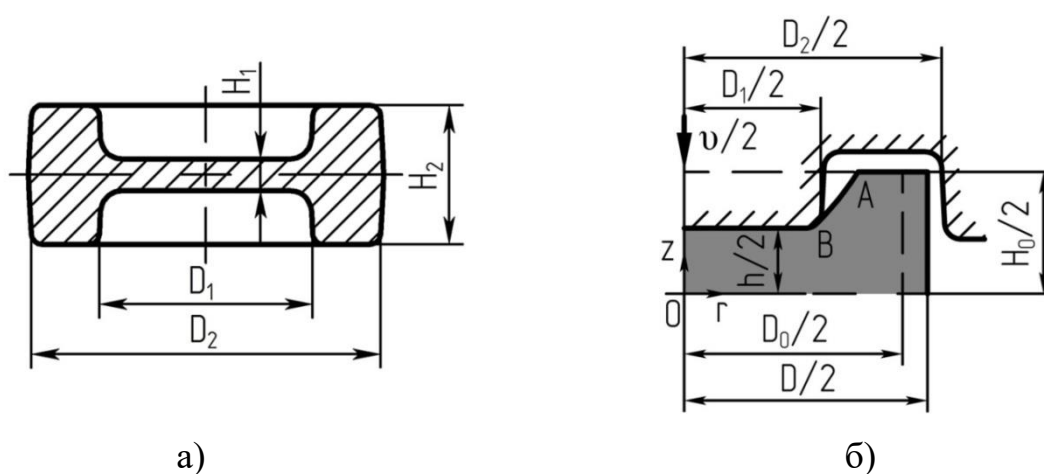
Кольцевая поковка с непробитой перемычкой без облоя (а) и схема формоизменения заготовки на первой стадии штамповки (б).
